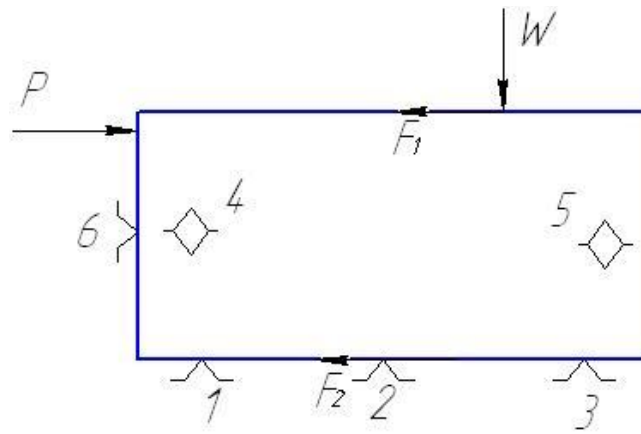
Схема сил, действующих на обрабатываемую деталь
